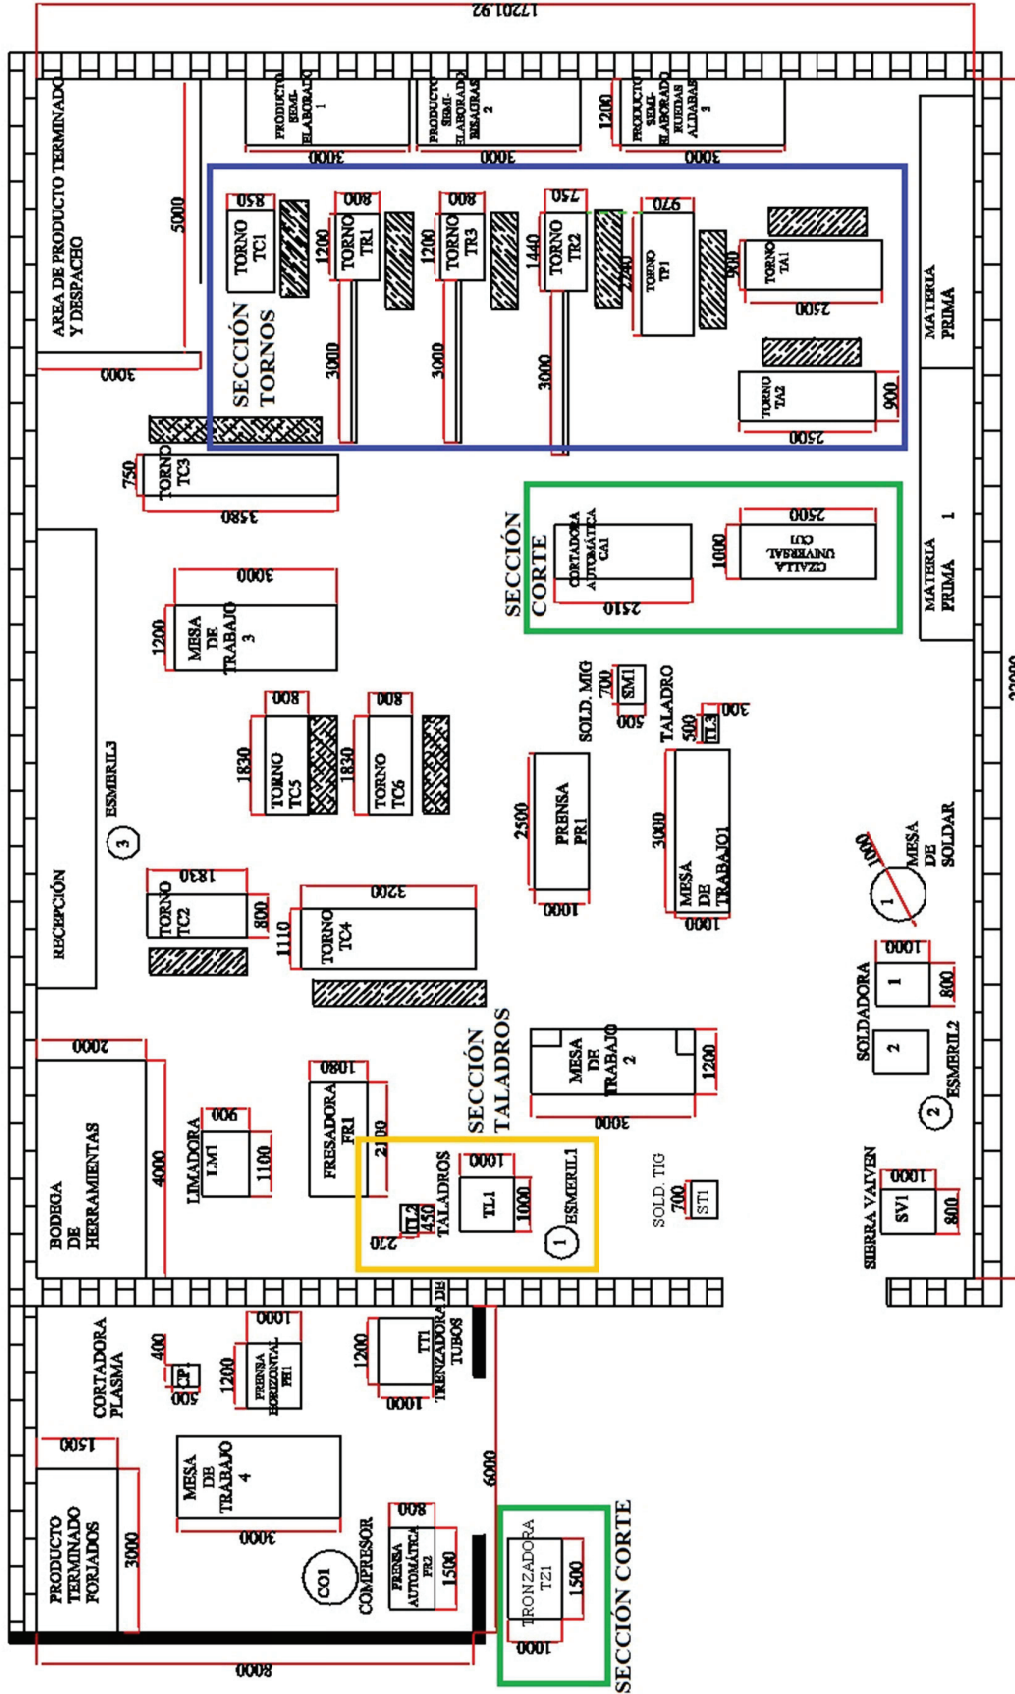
Mejoramiento de la distribución de planta. Layout propuesto
